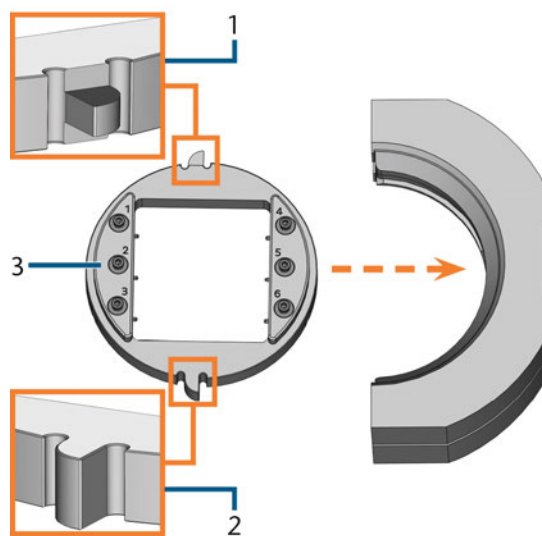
INSÉRER LE SUPPORT DE PIÈCES BRUTES CORRECTEMENT ORIENTÉ DANS LE SUPPORT DE PIÈCES BRUTES
